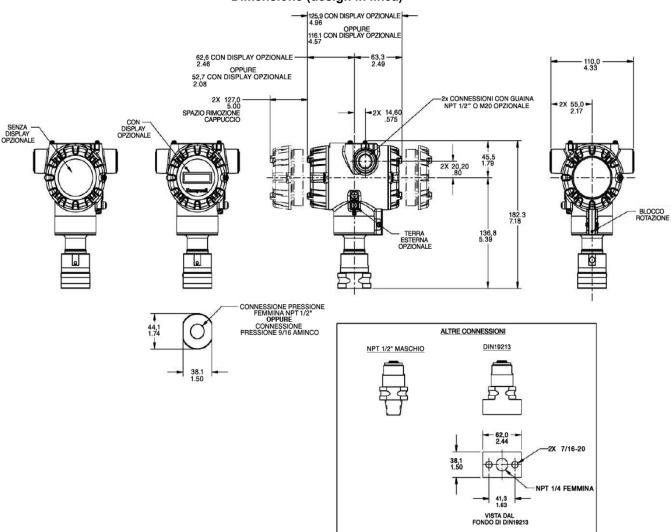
Dimensioni di montaggio tipiche di STA72L, STA74L e STA77L per riferimento
